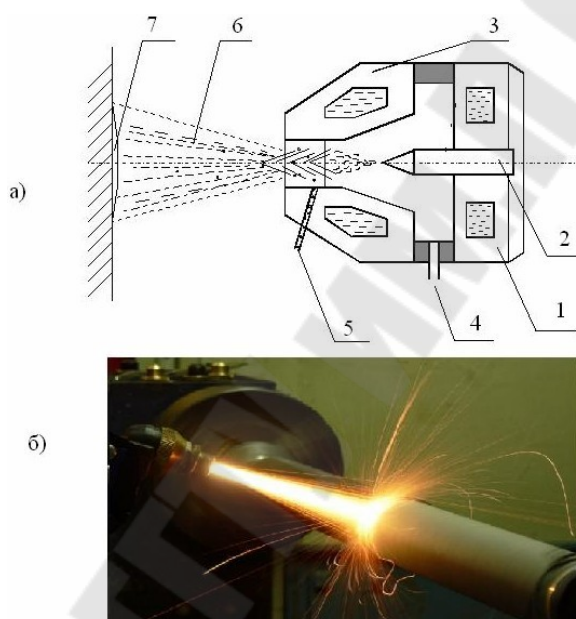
Схема (а) и реальный процесс (б) плазменно-порошкового напыления поверхностей деталей: 1 – корпус плазмотрона; 2 – вольфрамовый электрод;
